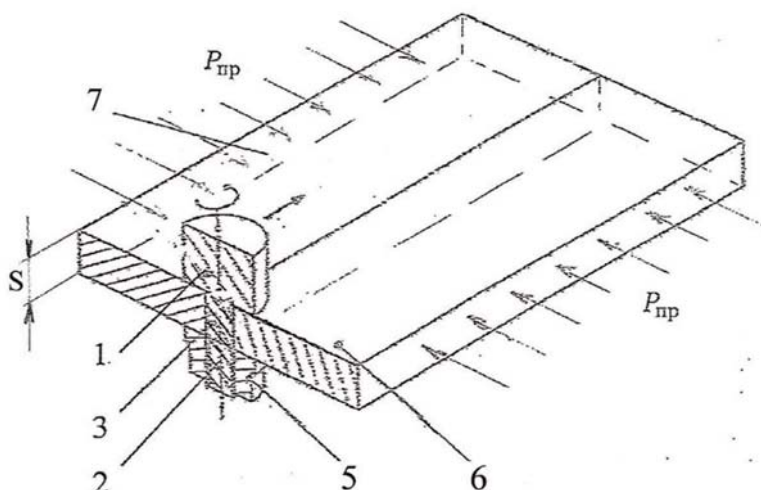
Схема работы инструмента: 1 – верхний корпус; 2 – стержень; 3 – зубчатая нарезка; 4 – кольцевой буртик; 5 – нижний корпус; 6, 7 – листовые заготовки
